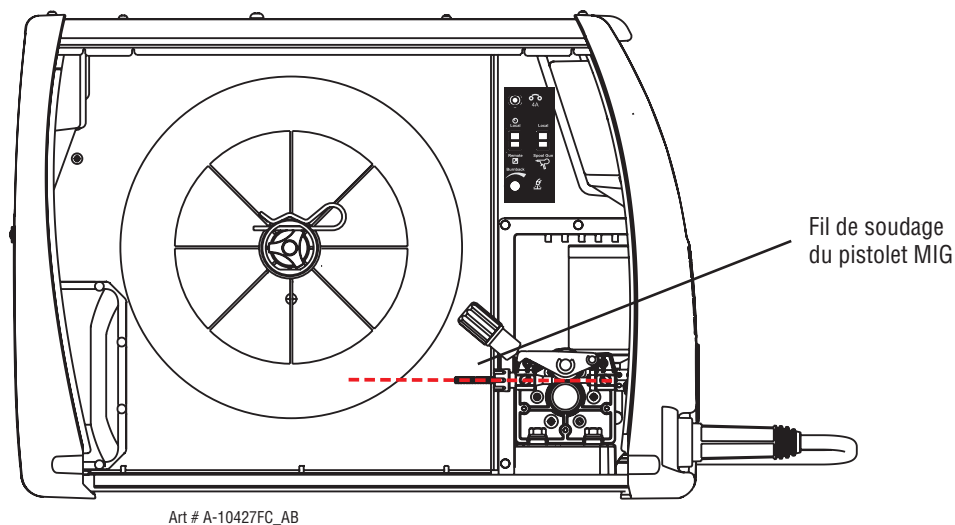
Fil de soudage MIG - Pose
